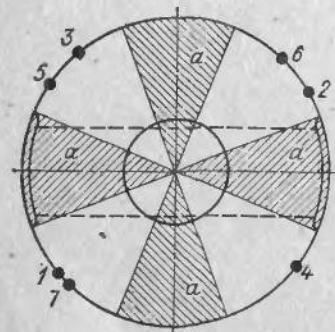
Схема установки замков поршневых колец: 1—7 — расположение замков поршневых колец (нумерация колец сверху вниз)
